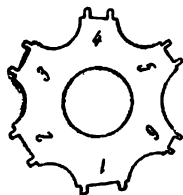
Ключ для отвертывания накладки барабанного колеса
